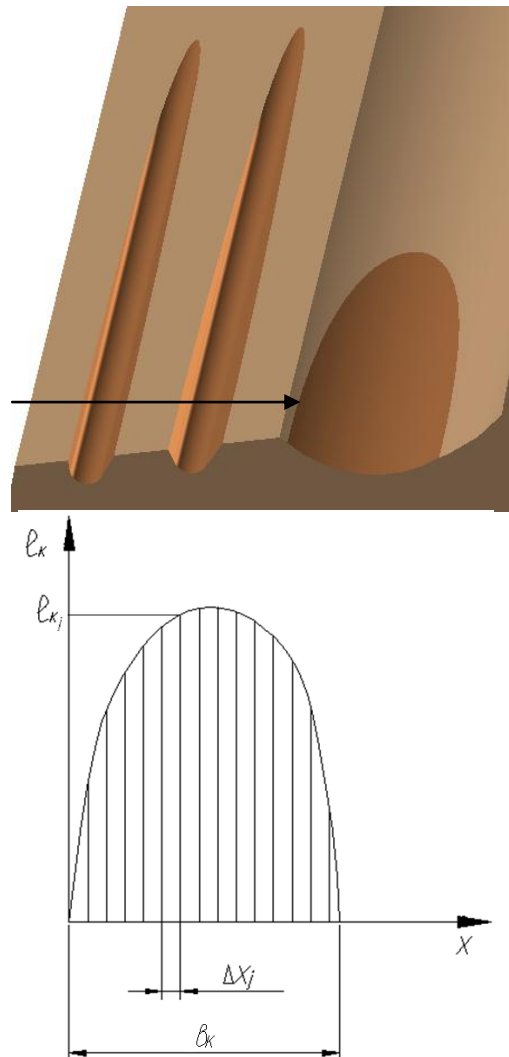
Разбиение поверхности соприкосновения инструмента и заготовки на участки Δx_j
